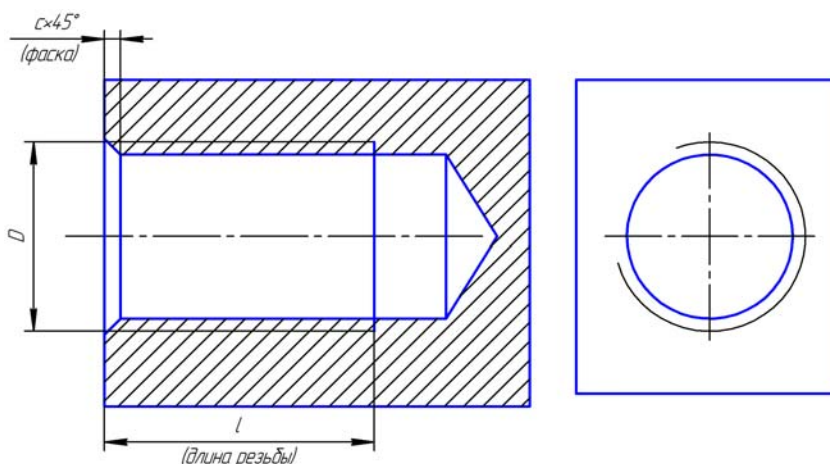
Изображение резьбы в глухом цилиндрическом отверстии
